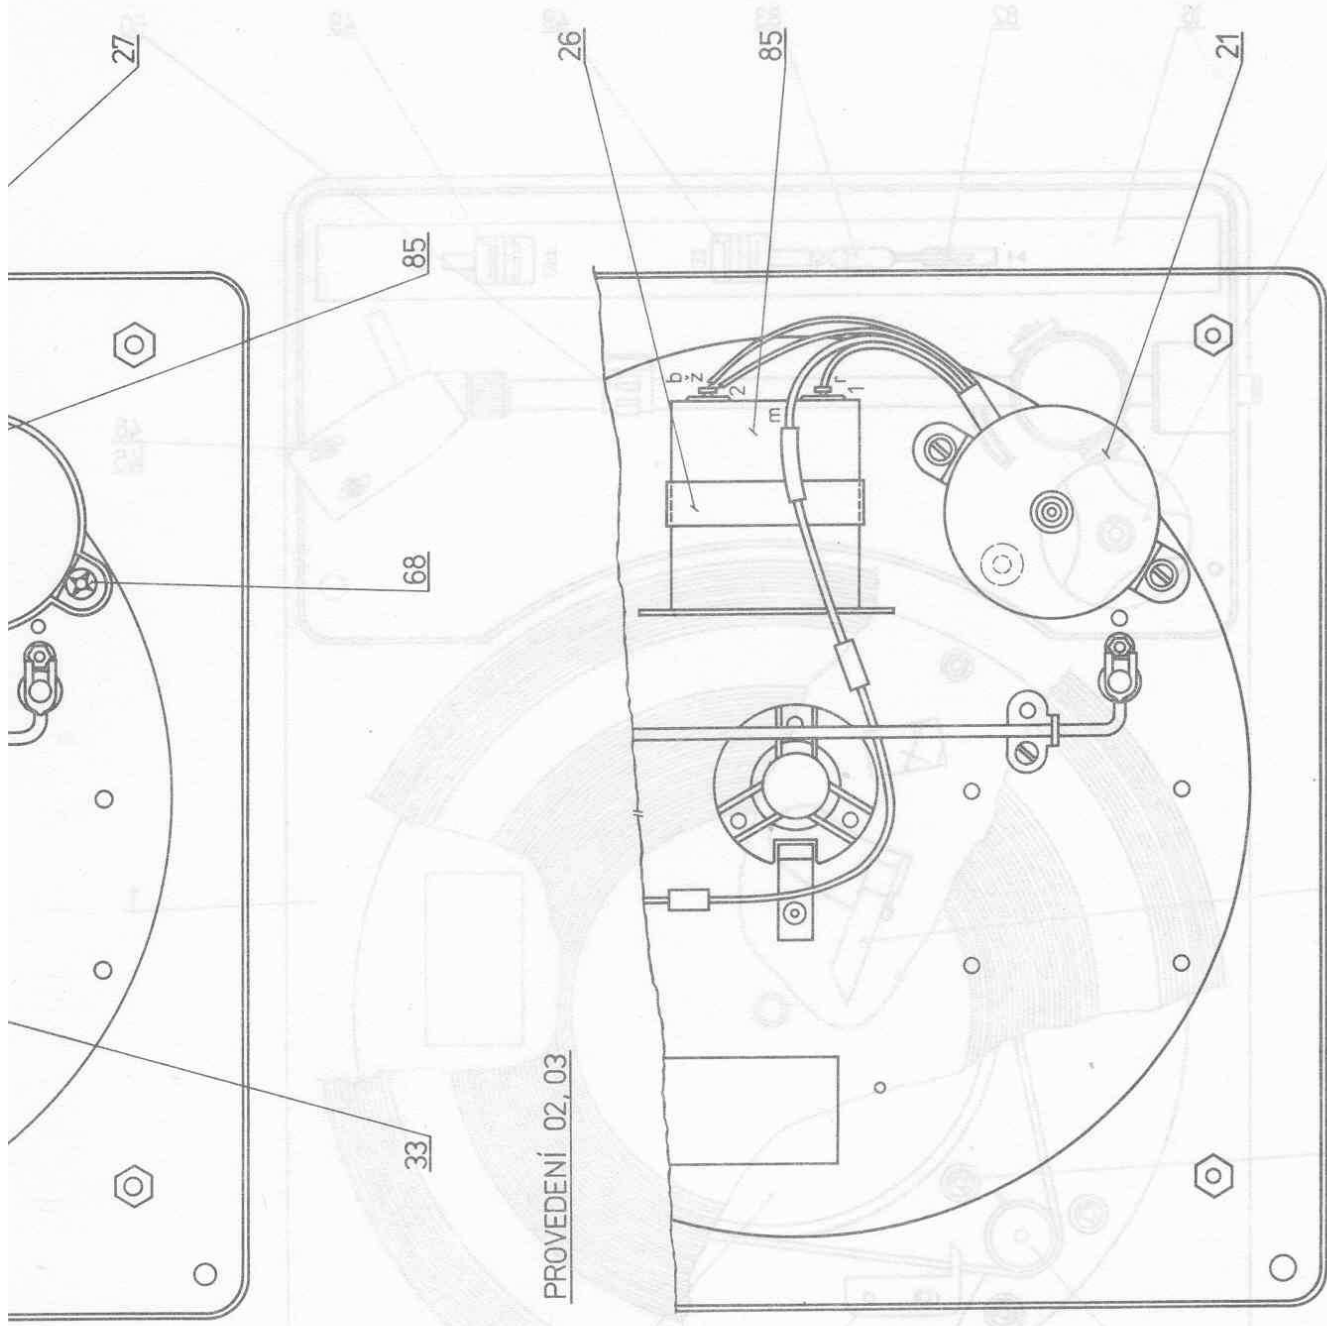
Mechanické a náhradní díly HC 16- pohled z boku
